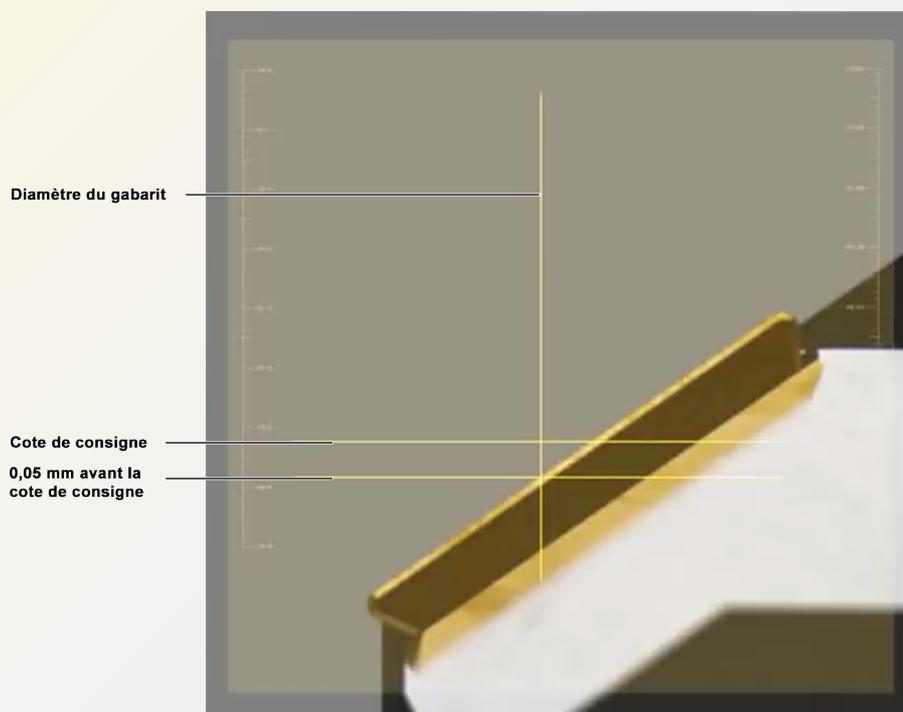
PCR réglée sur 0,05 mm de moins que la cote de consigne
